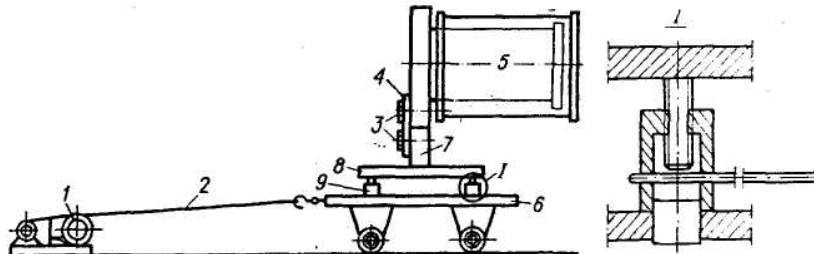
Пристрій для витягування трубочки з горизонтального теплообмінника:
